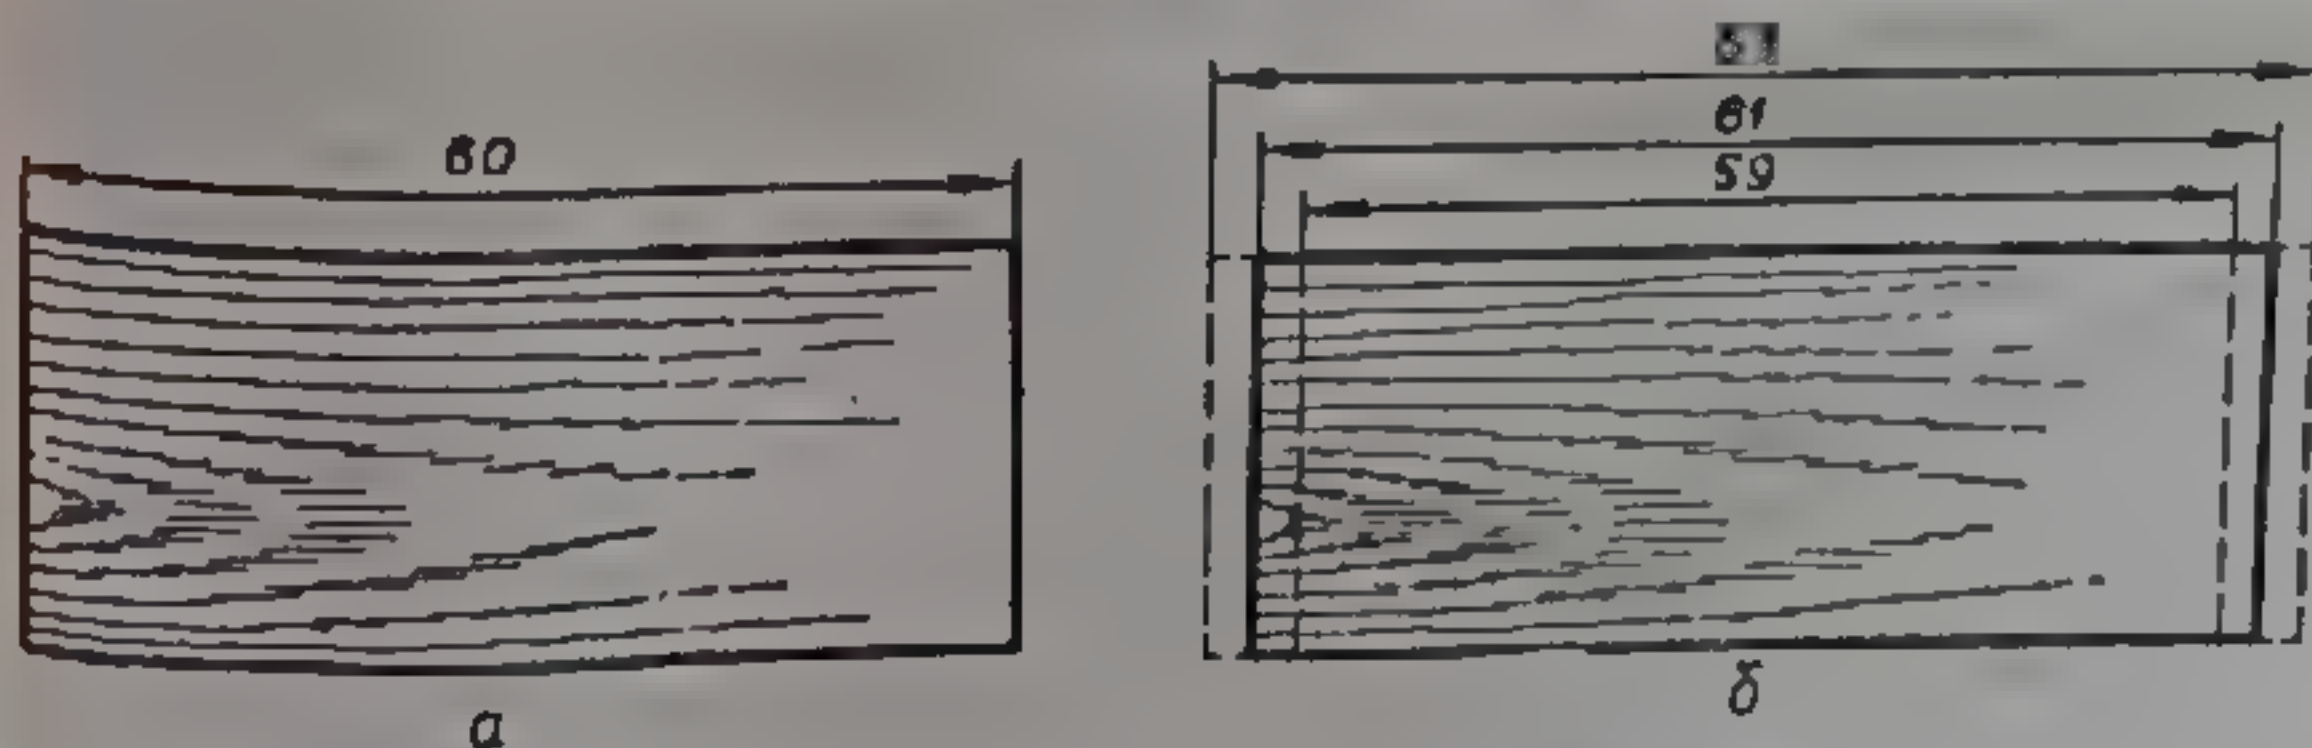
Номинальный (а) и предельные (б) размеры деталей: 60 мм — номинальный размер на чертеже; 61 мм — действительный (измеренный) размер; 63 мм — наибольший допустимый размер; 59 мм — наименьший допустимый размер.
